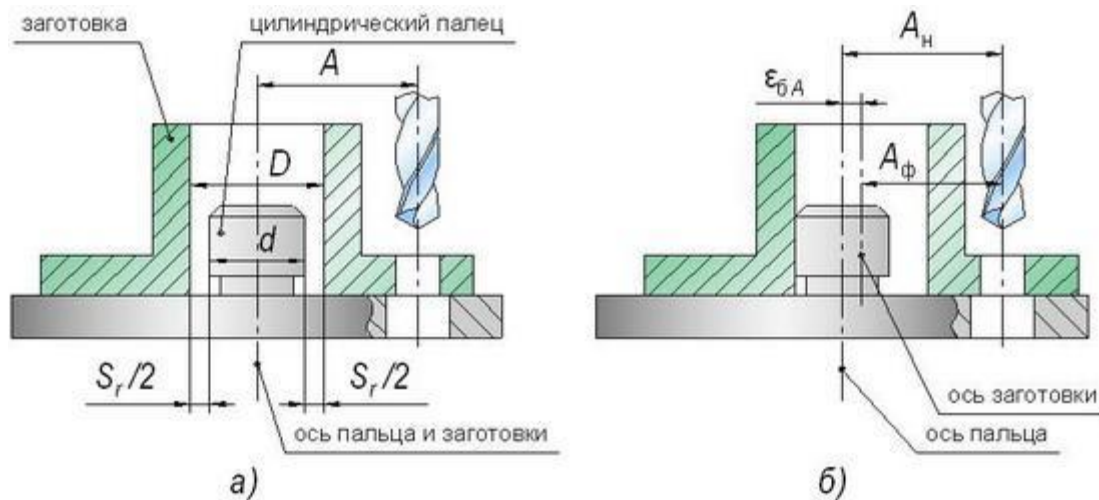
Сверление отверстия ступицы: *a* - зазор распределен равномерно; *б* - зазор распределен с одной стороны; A , A_n - размер наладки сверла; $A_ф$ - фактический размер, получаемый при сверлении; d - диаметр цилиндрического пальца; D - диаметр отверстия заготовки
